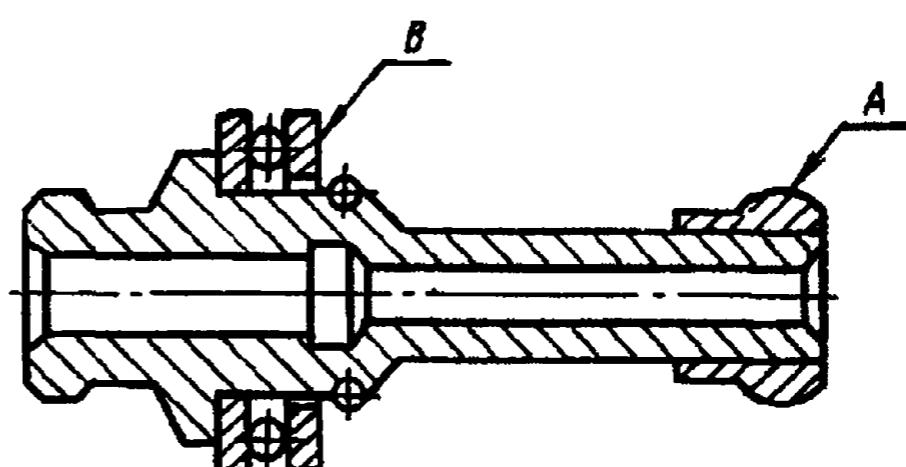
Муфта грузов регулятора с подшипником в сборе
